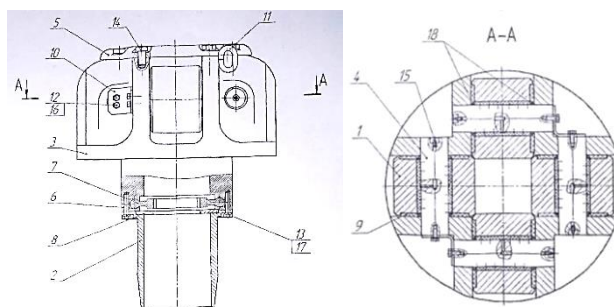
Вкладыш роликовый. 1 — ролик в сборе; 2 — труба направляющая; 3 — корпус; 4 — ось; 5 — крышка; 6 — диск; 7 — обтиратель; 8 — сектор квадратный; 9 — диск торцевой; 10 — скоба; 11 — ушко; 12, 13, 14 — болт; 15 — масленка; 16, 17 — шайба; 18 — уплотнения
